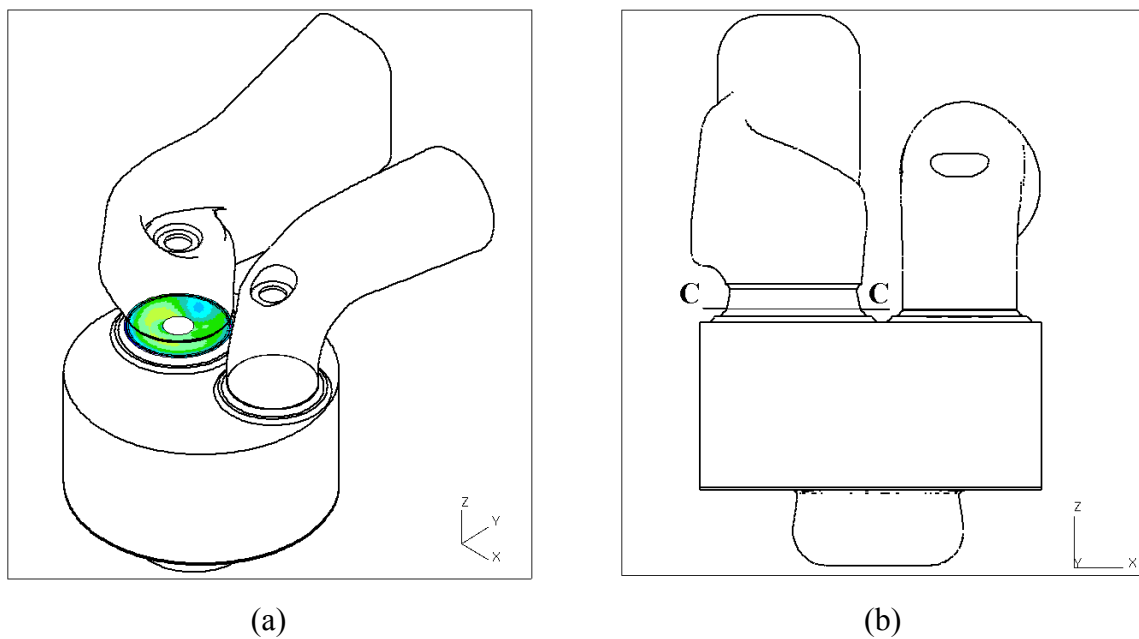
Corte C-C: (a) vista isométrica; (b) vista frontal
